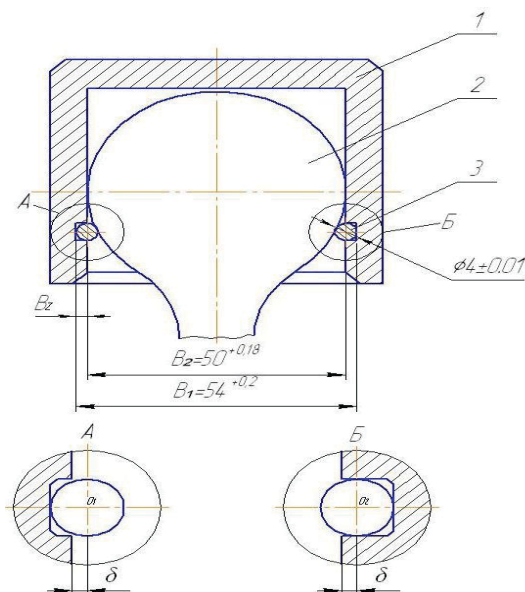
Схема крепления гидроцилиндра к платформе: А – положение центра кольца при B_{Zmin} ; Б – положение центра кольца при B_{Zmax} ; 1 – стакан; 2 – шаровая головка гидроцилиндра; 3 – стопорное кольцо.
